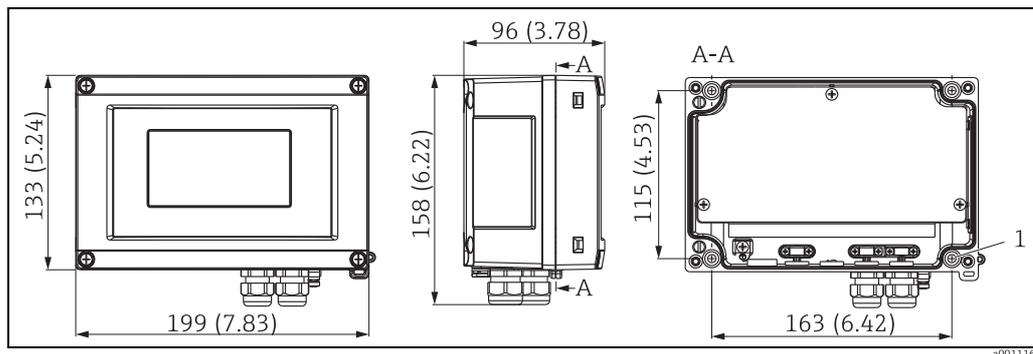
Dimensioni di installazione; dimensioni in mm (in)
